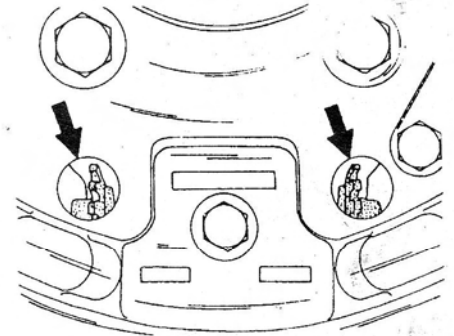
Стрелки указывают положение установочных шестерен регулировочного механизма Mercedes - Benz.
